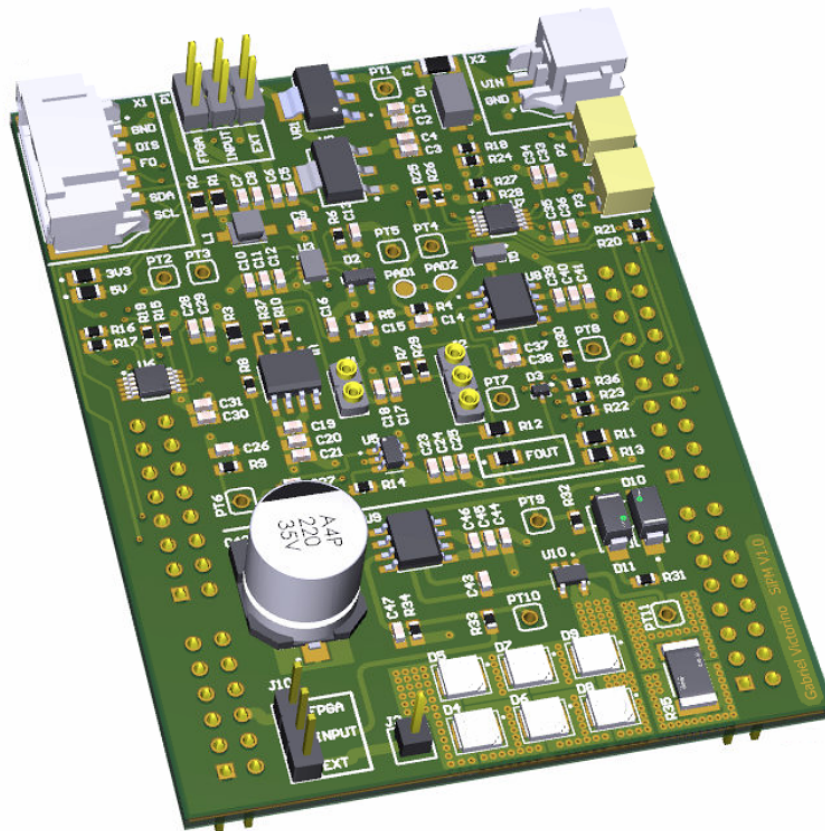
Imagem 3D da PCB finalizada. Fonte: Autor.
